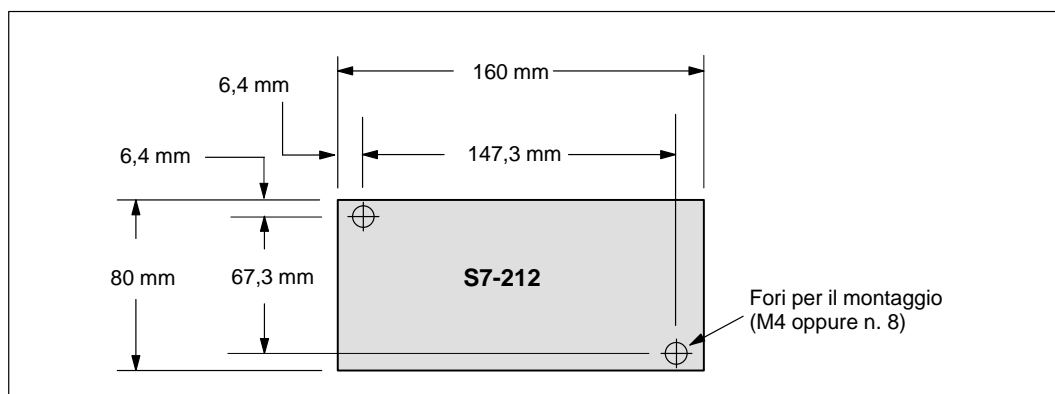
Dimensioni per il montaggio di una CPU S7-212
